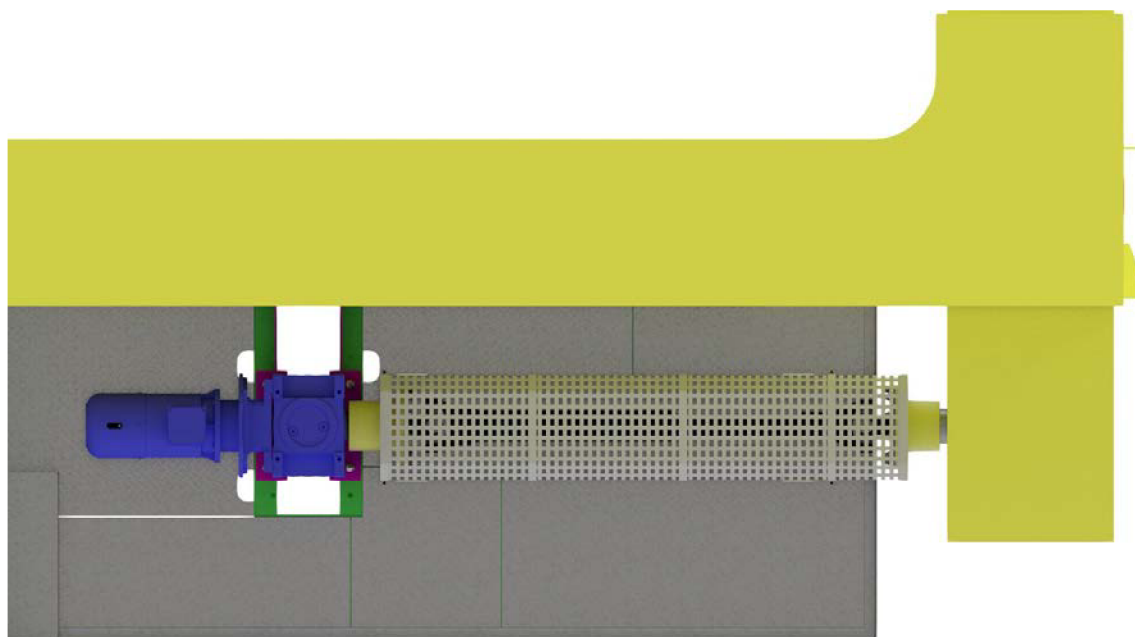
Mechanismy pojezdu – IZO pohled 3
